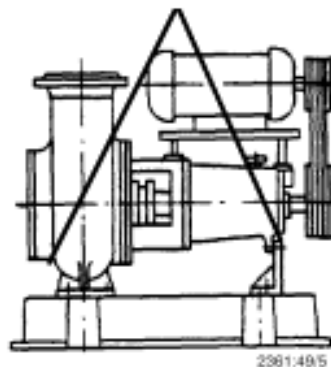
Транспортировка насосного агрегата в сборе
